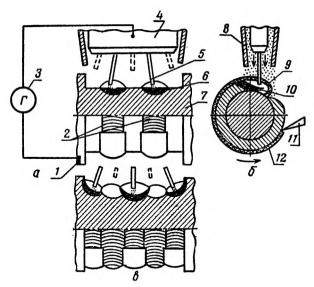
Схема многоэлектродной наплавки в раздельные сварочные ванны:
